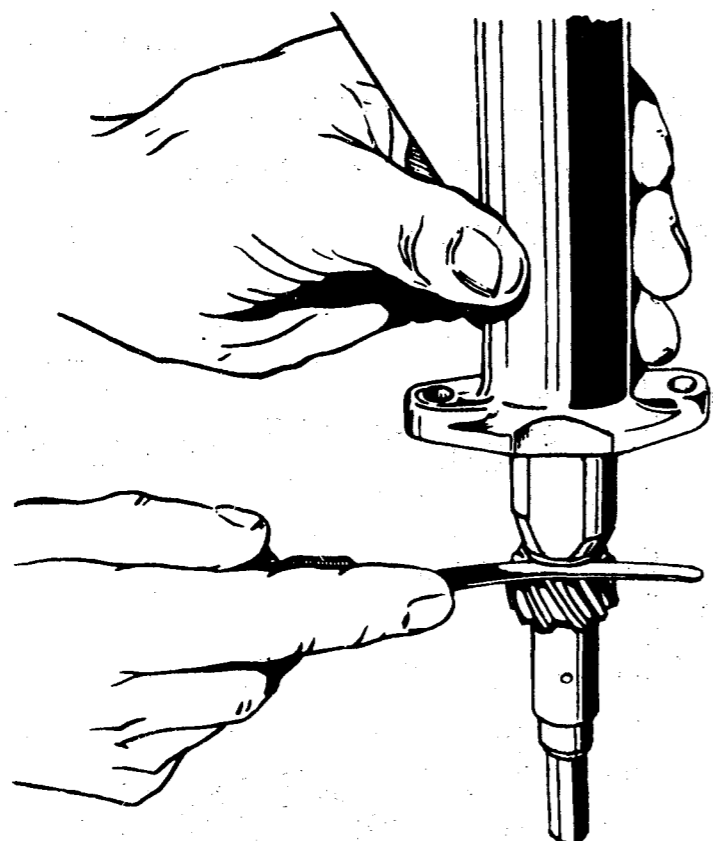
Проверка осевого зазора между корпусом привода масляного насоса и распределителя зажигания и шестерней
